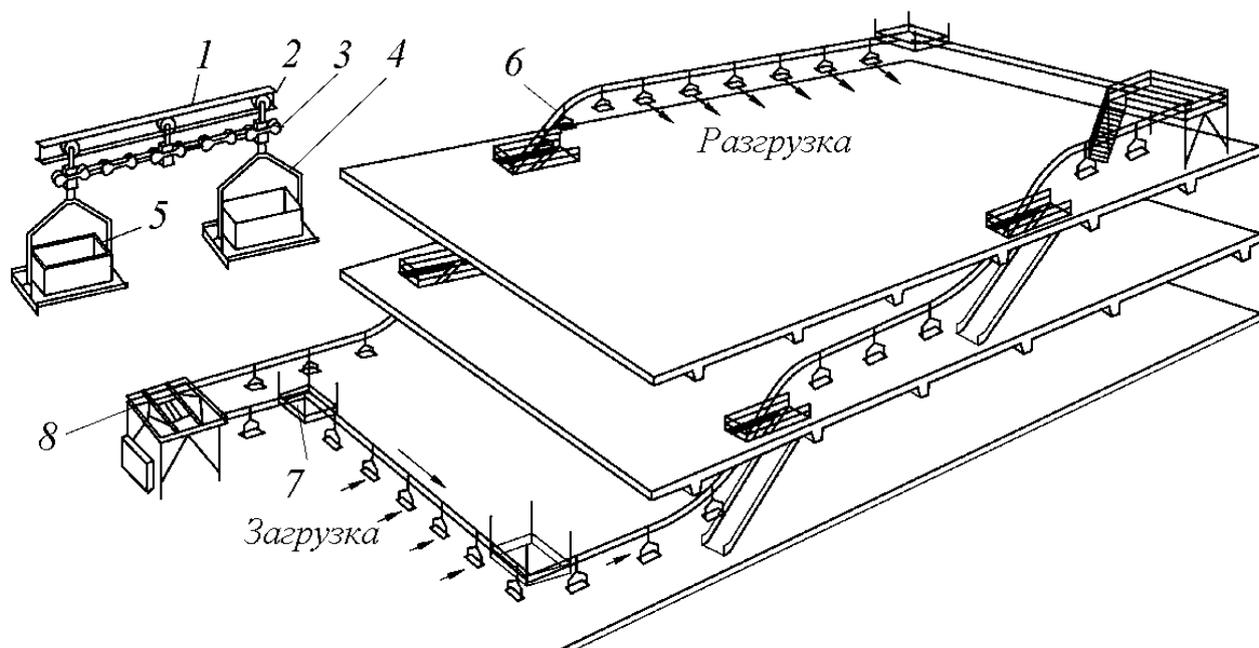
Общий вид подвесного грузонесущего конвейера:
